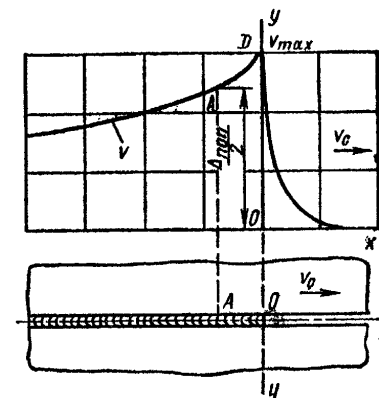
Схемы образования поперечной усадки при однопроходной стыковой сварке
